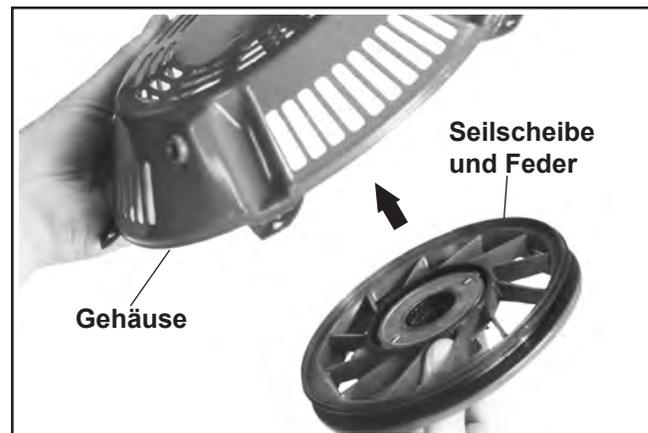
Installation der Seilscheibe und der Feder im Gehäuse.
